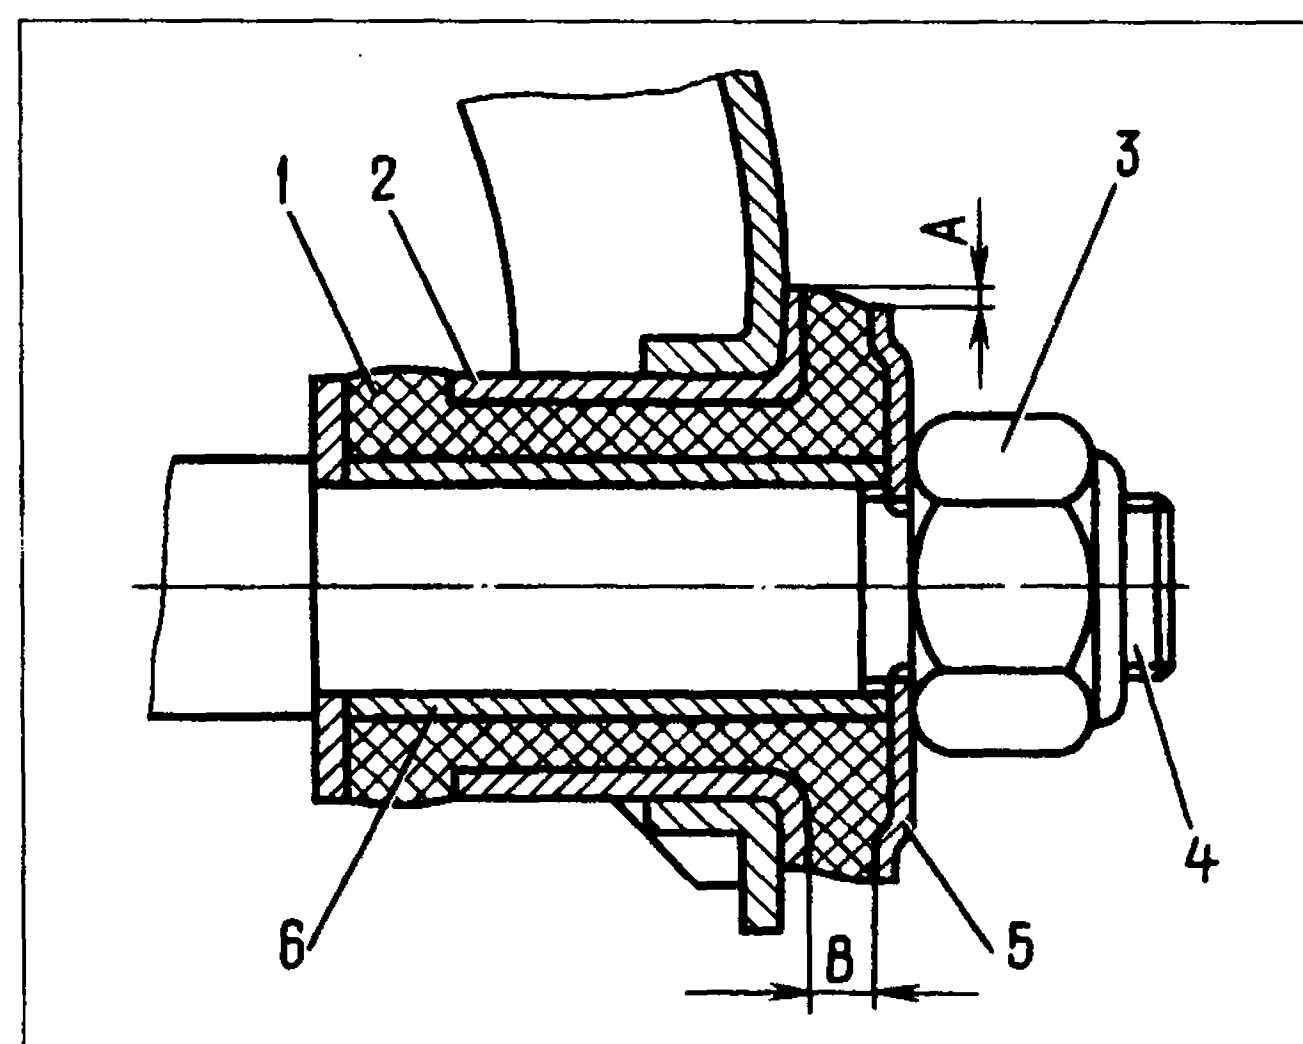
Проверка состояния резинометаллического шарнира рычага передней подвески:
